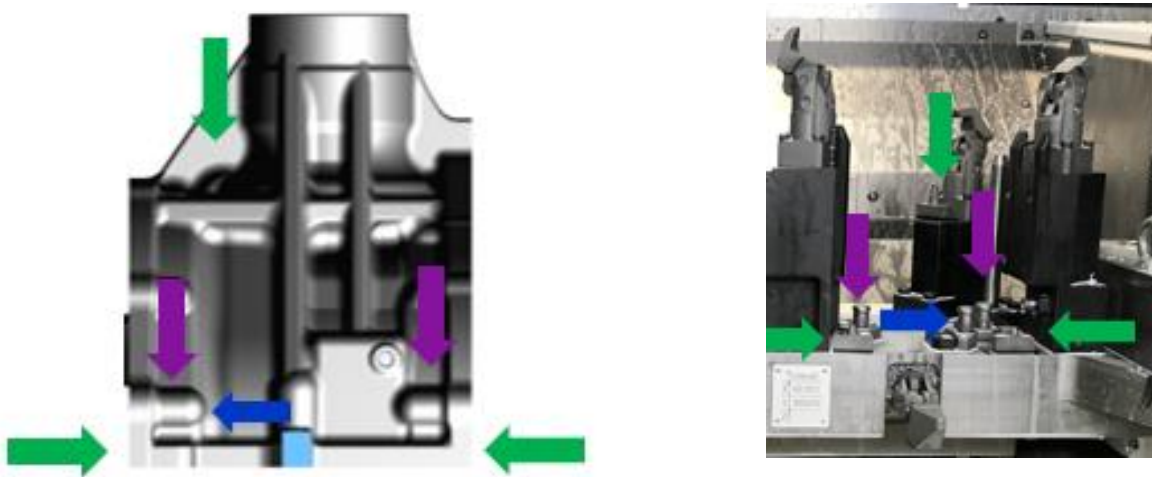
Zona de asiento de carrier en dispositivo de maquinado de la primera operación.
